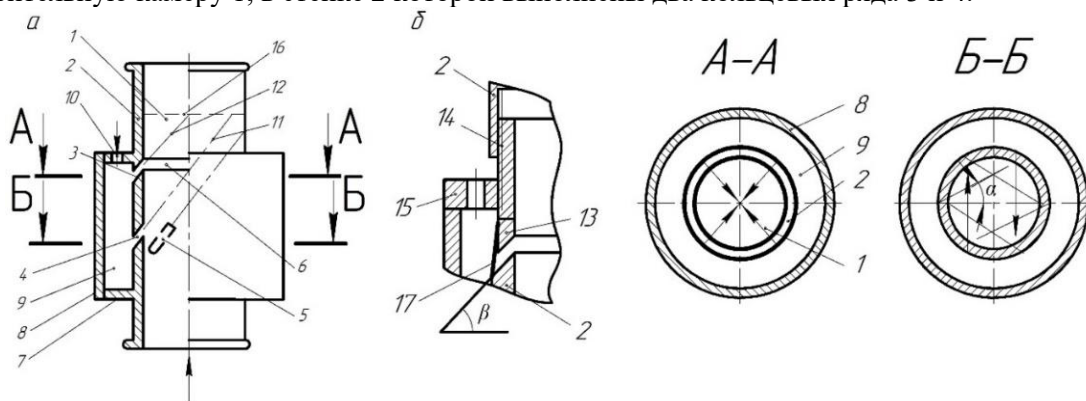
Схема подъёмного устройства: а - общий вид устройства; б - узел резьбового крепления кольцевого патрубка 13 к фланцу 15 секции 7 нагнетания воздуха; 1 - смесительная камера; 2 - стенка смесительной камеры; 3 - кольцевой ряд сквозной поперечной щели 6; 4 - кольцевой ряд сквозных отверстий 5; 7 - секция цилиндра; 8 - стенка цилиндра; 9 - круговой зазор; 10 - отверстие; 11 - ось сквозного отверстия; 12 - наклон по потоку движения среды; 13 - патрубок; 14 - резьбовое соединение; 15 - съёмный фланец; 16 - поперечное сечение; 17 - сетка для улавливания загрязнённого сжатого воздуха
